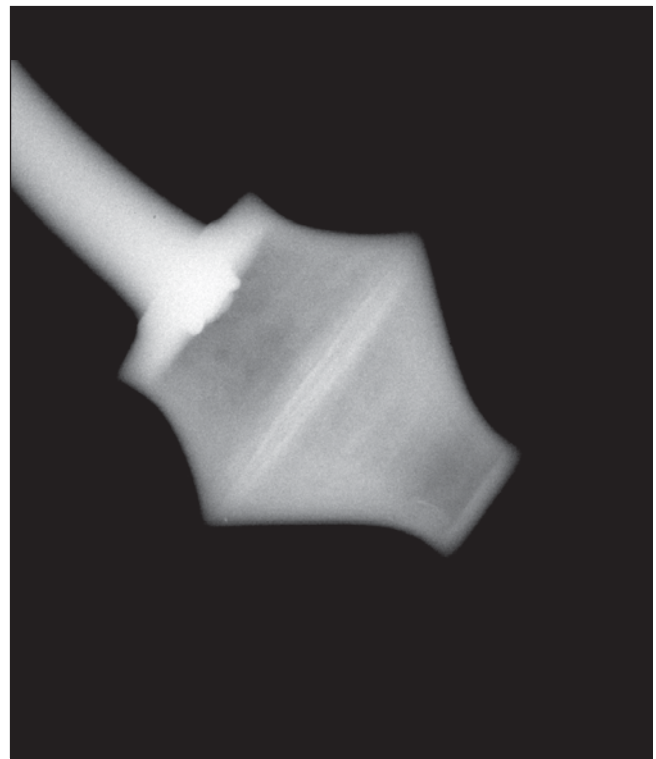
Sistema de soldadura del brazo en el interior de una doble escoria.
